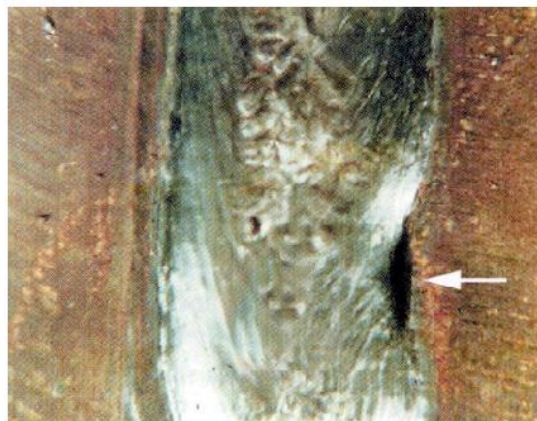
Falta de fusión en la superficie de la soldadura. (Ruiz, 2016)
